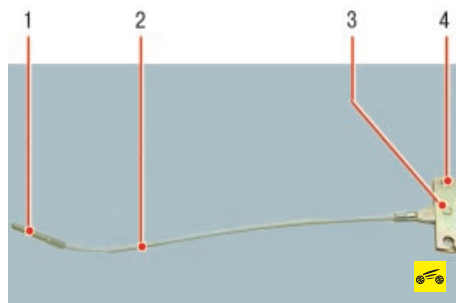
Детали уравнивателя привода стояночного тормоза: 1 – резьбовой хвостовик; 2 – тросовая тяга; 3 – заклепочная ось; 4 – коромысло
